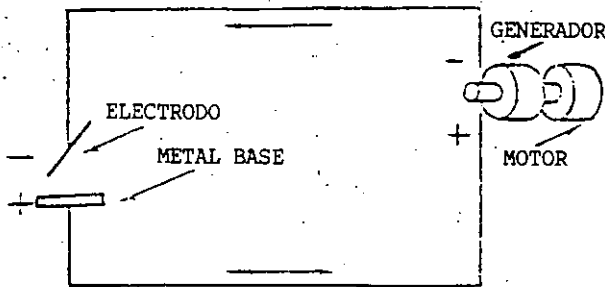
FIG. _____ CIRCUITO DE SOLDADURA DE ARCO CON ELECTRODO METALICO.
